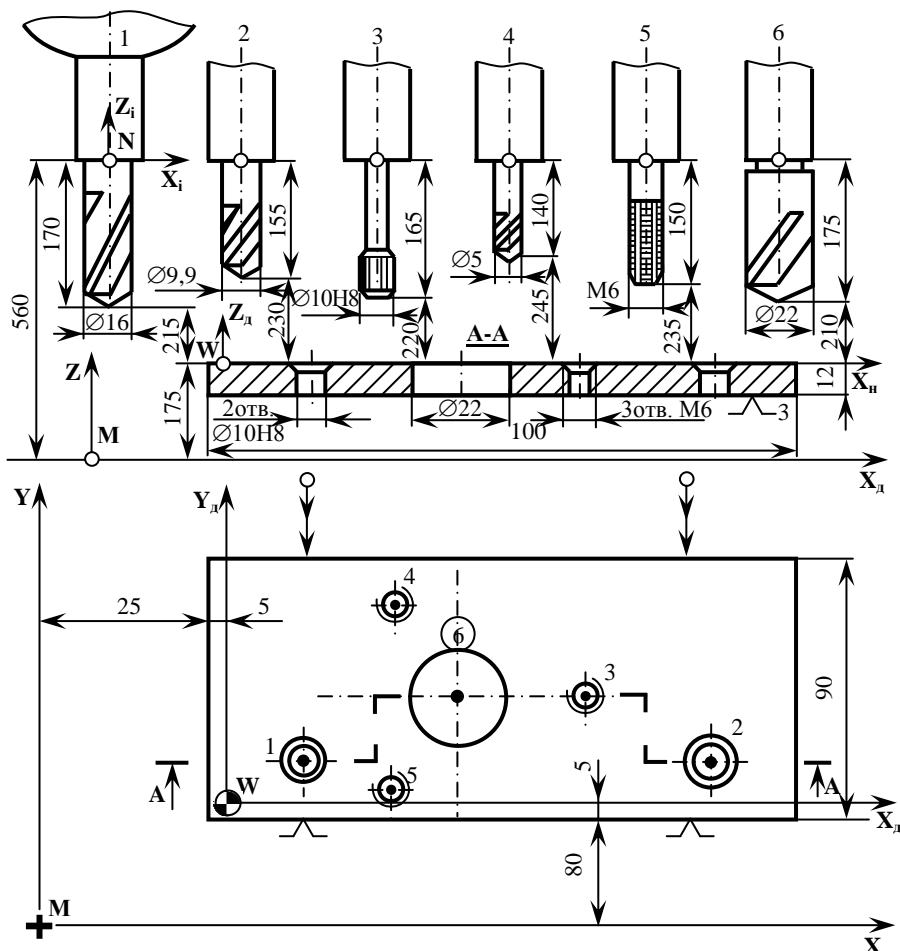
Схеми для підготовки РТК при обробці отворів у деталі типу кришка
